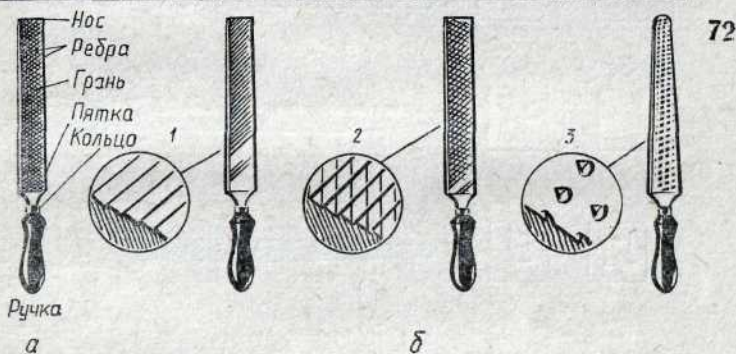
Напильник: а — общий вид; б — профили насечек; 1 — одинарная насечка; 2 — двойная насечка; 3 — рашпильная насечка.
